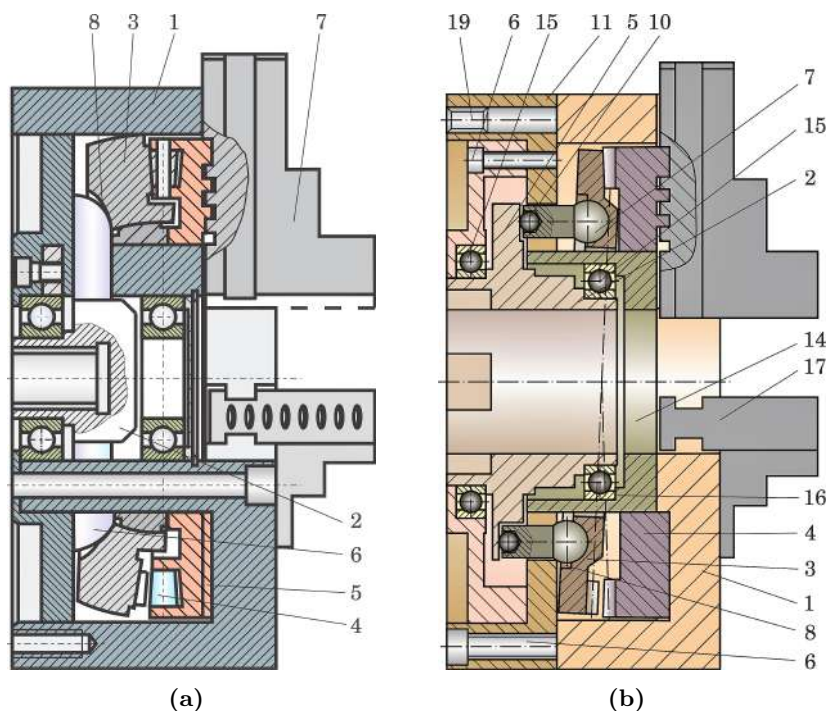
Transmisie precesională  $2K-H$  cu hidromotor axial cu pistoane în sinteză
